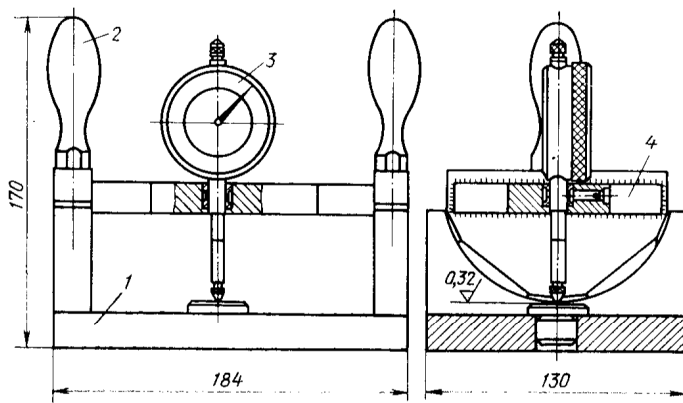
Контрольное приспособление для подбора толщины регулировочных шайб: 1 — корпус; 2 — ручка; 3 — индикатор; 4 — основание
